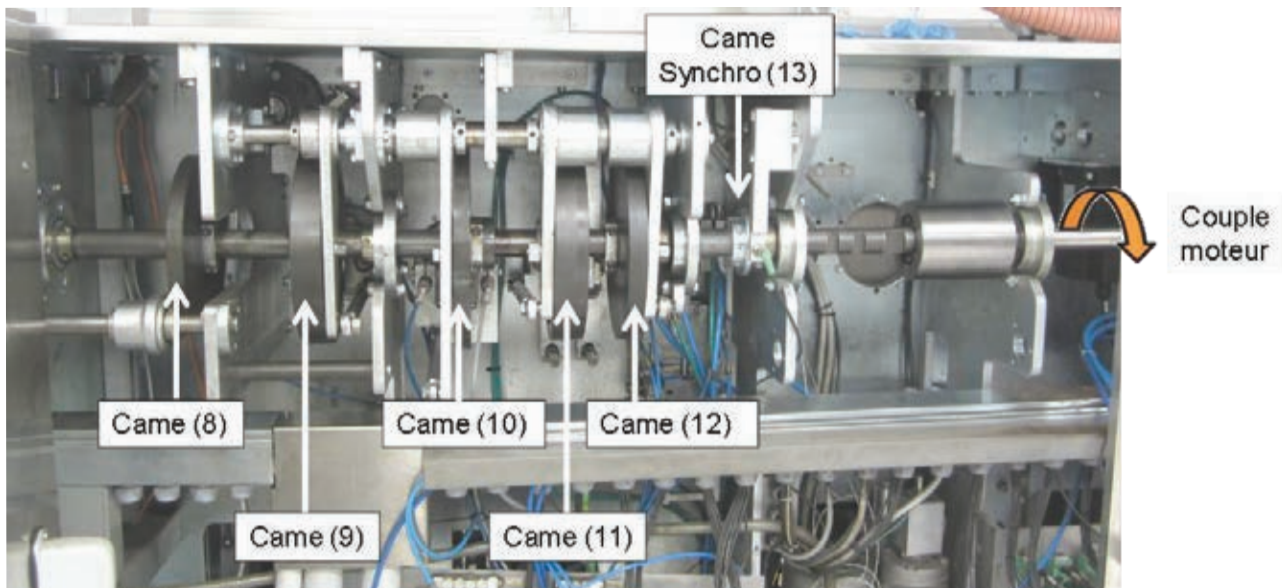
Arbre à cames – Face arrière de la remplisseuse
